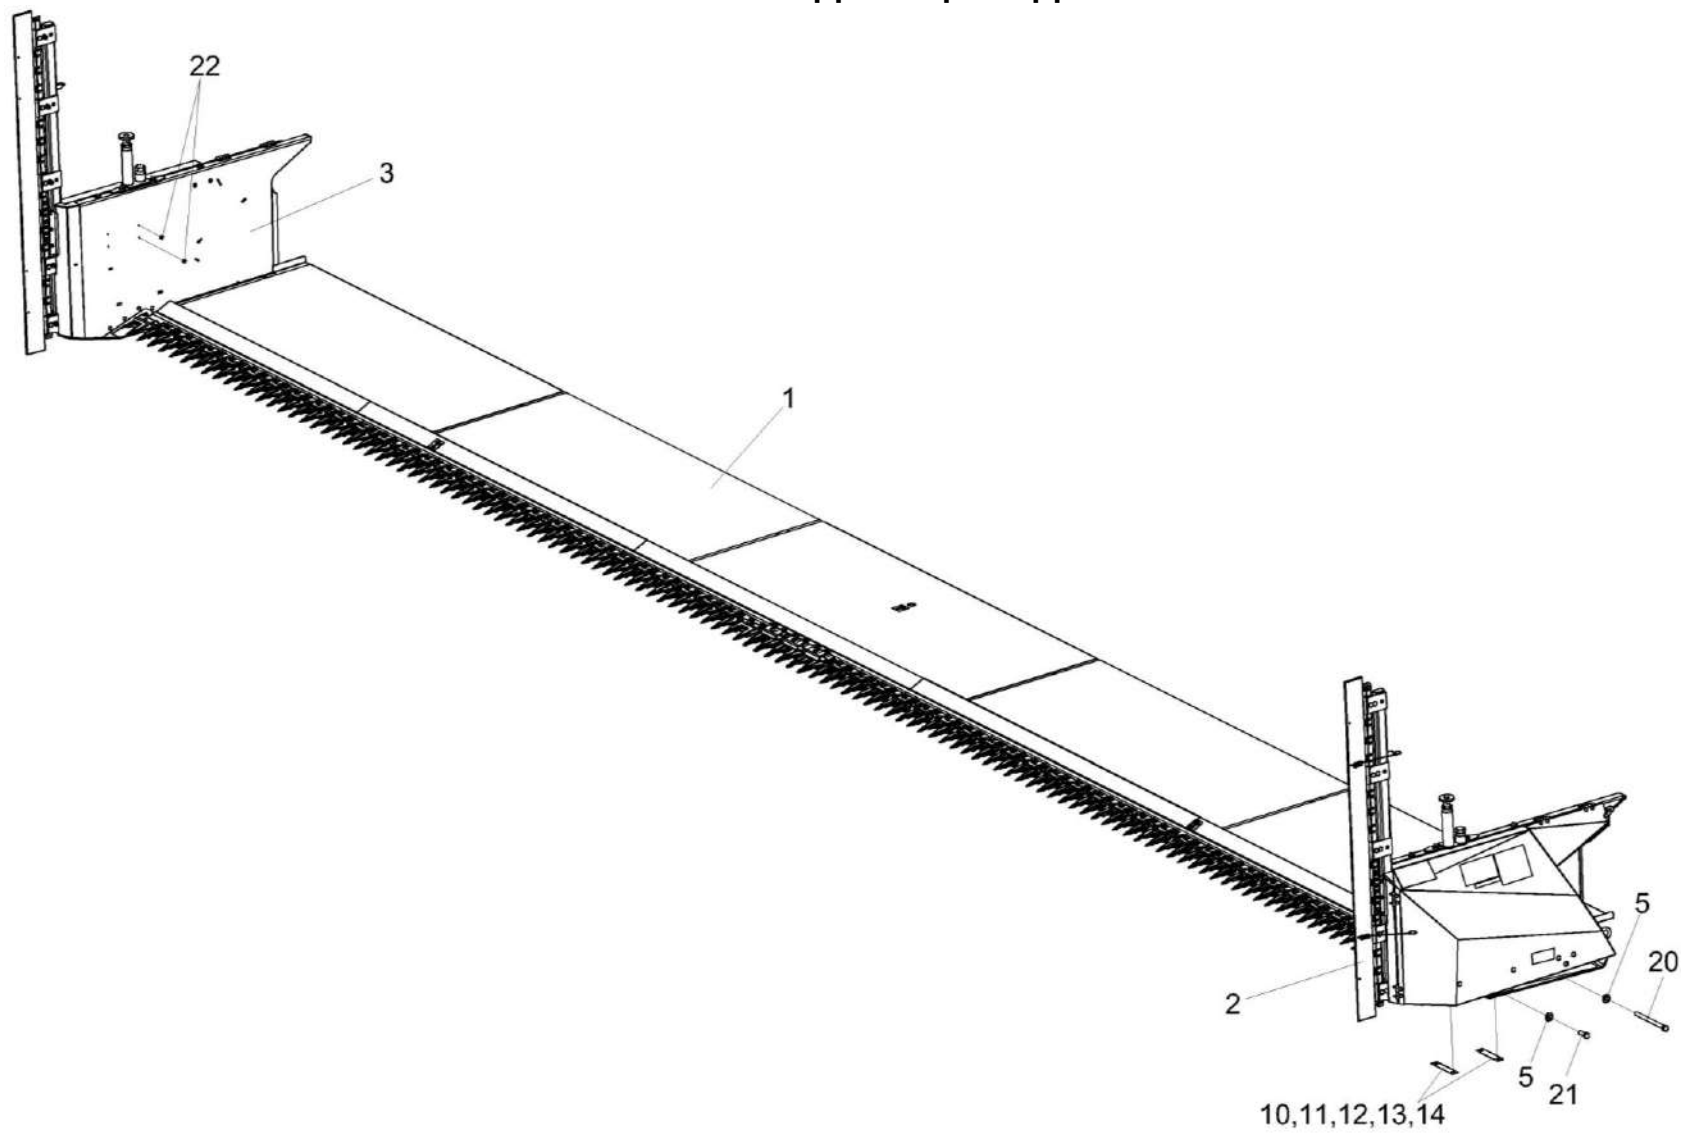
Приспособление для уборки рапса ПР-9 КЗК-9-2540000
